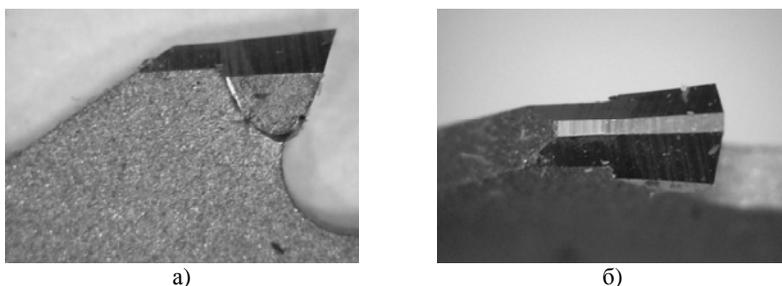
Твердосплавные пилы: вид сбоку (а); вид сверху (б)
